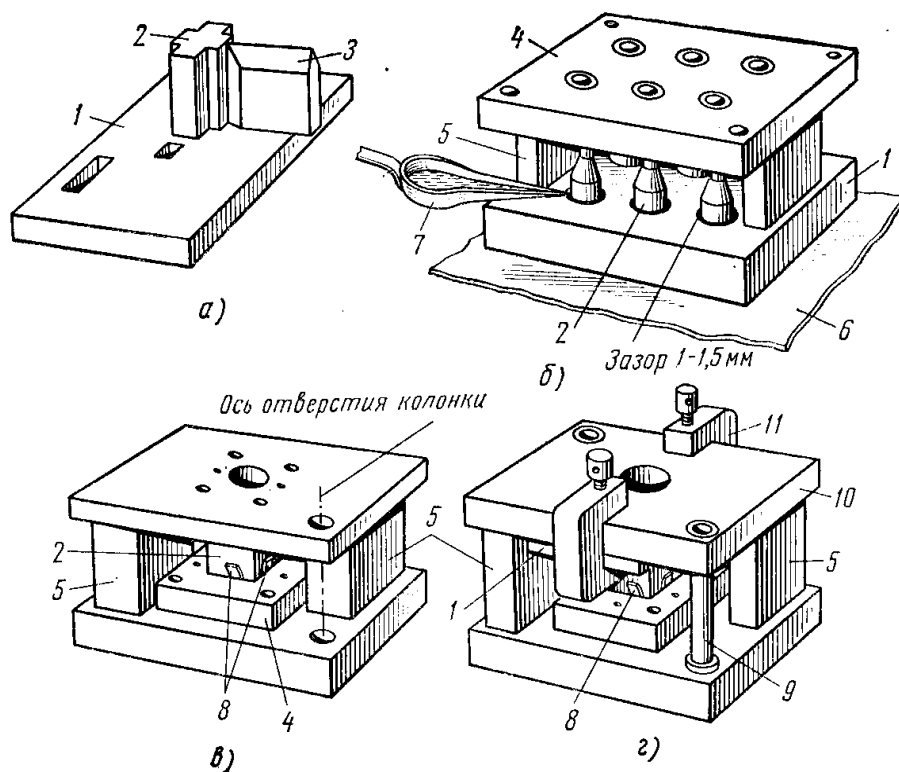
Примеры сборки штампов: *а* – установка пуансона в пуансонодержатель, *б* – заливка пуансонов расплавленным сплавом, *в, г* – способы установки пуансонодержателя; 1 – пуансонодержатель, 2 – пуансон, 3 – лекальный угольник, 4 – матрица, 5 – подкладка, 6 – асбестовая прокладка, 7 – ковш, 8 – фольга, 9 – колонка, 10 – верхняя плита, 11 – струбцина
